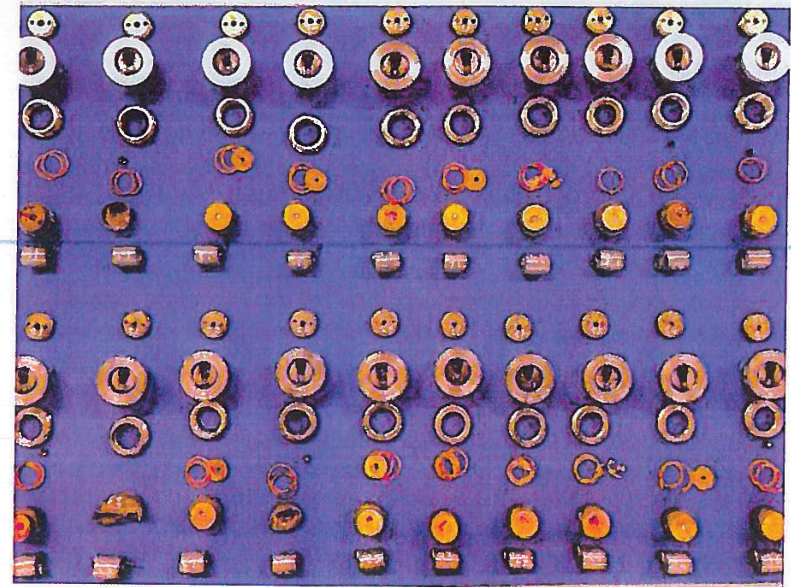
Details gemodificeerde schokbuis M6-H na de doorslagtest (Foto: KC W&M)
